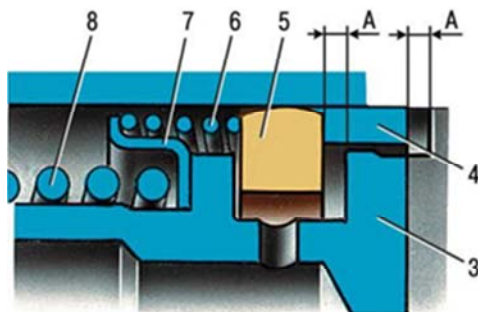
Фрагмент главного тормозной цилиндр автомобиля ВАЗ-21186:
